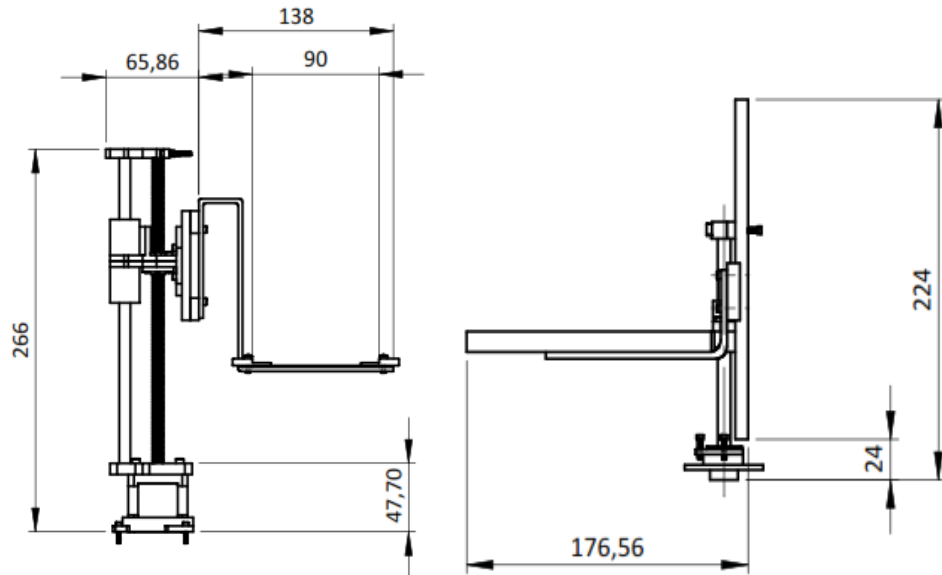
Esquema frontal dimensional del sistema mecánico de la impresora.
